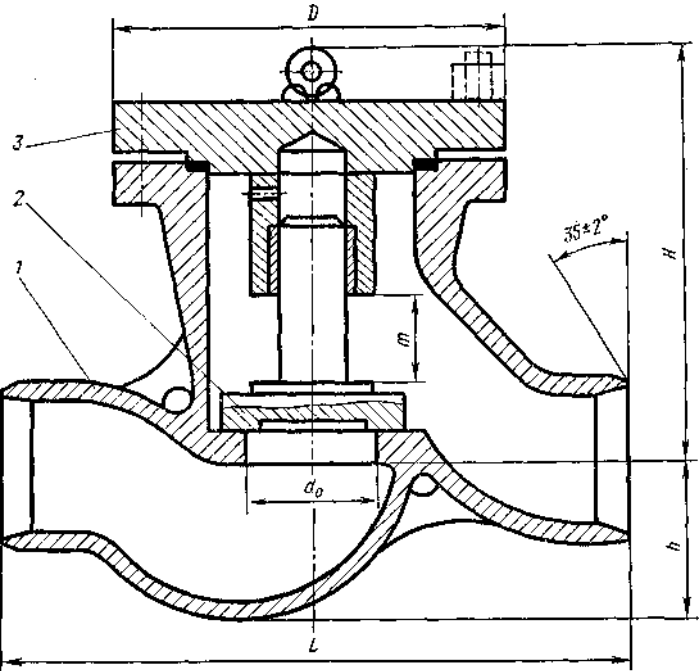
Обратный клапан подъемный Т-186 и Т-1186
